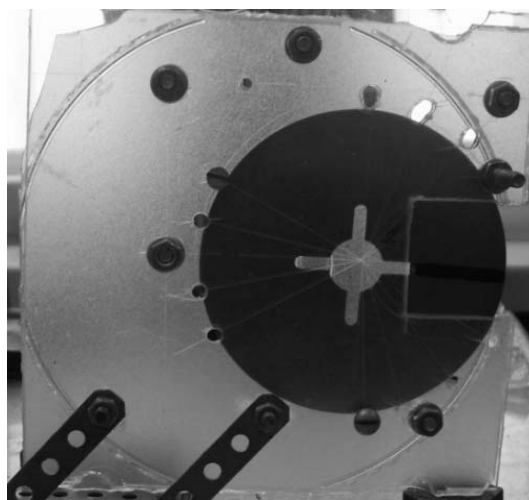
Фотография общего вида кассеты для бесцентрового шаржирования диска
